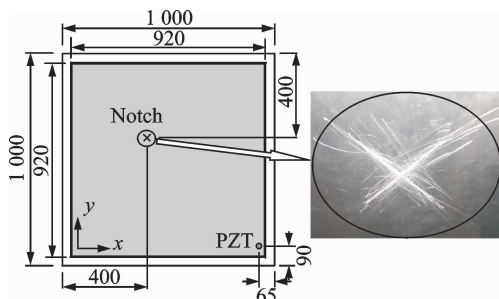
铝板平面尺寸及划痕布置图(单位: mm)
